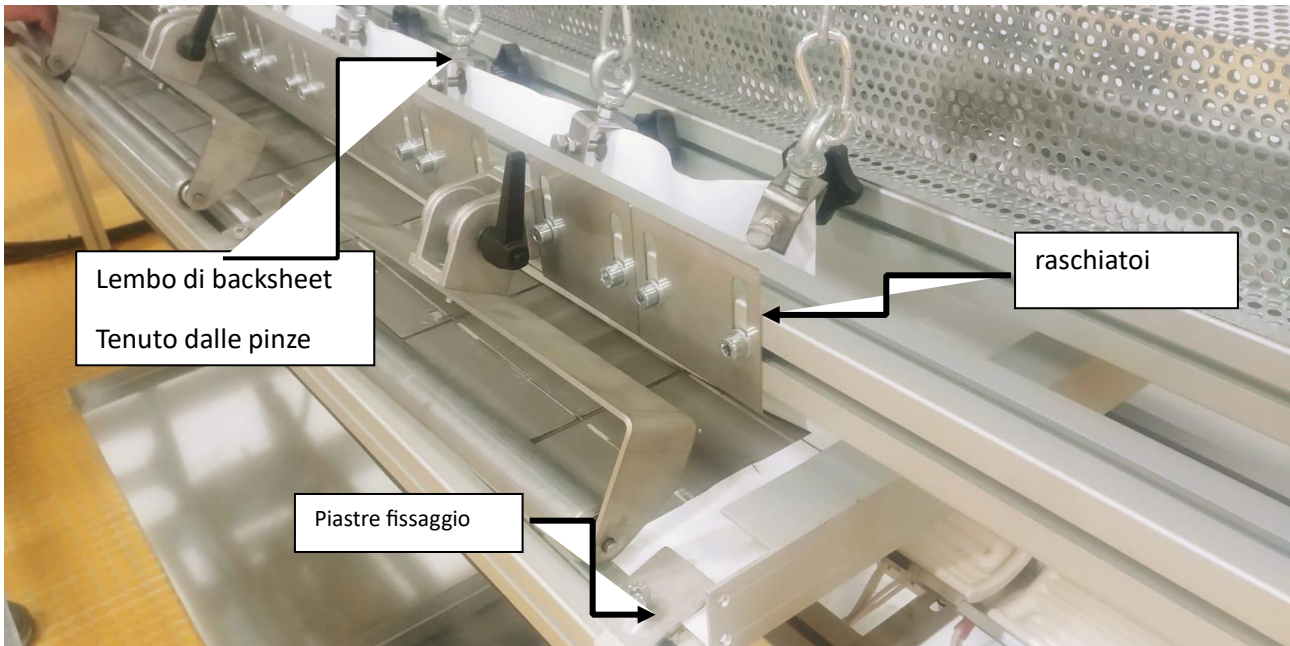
Fissaggio del pannello sul prototipo e assicurazione del lembo di backsheet tramite pinze di afferraggio
